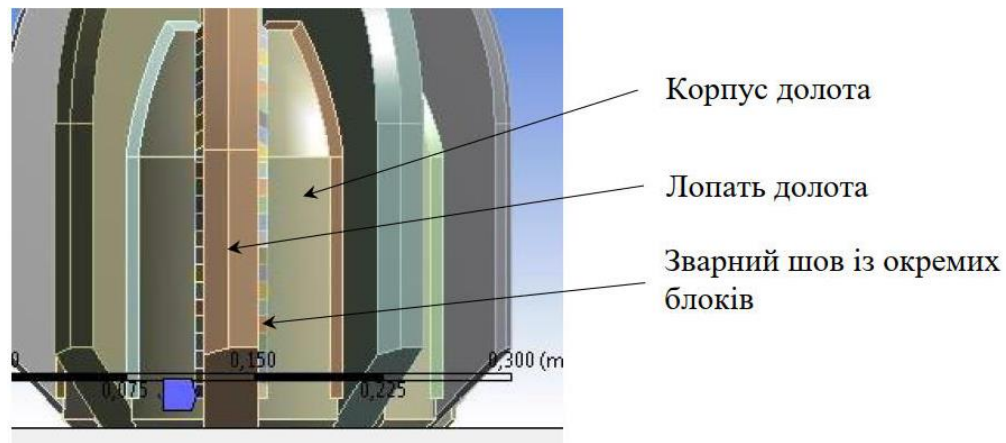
3-D модель зварного шва привареної лопаті до корпусу долота
